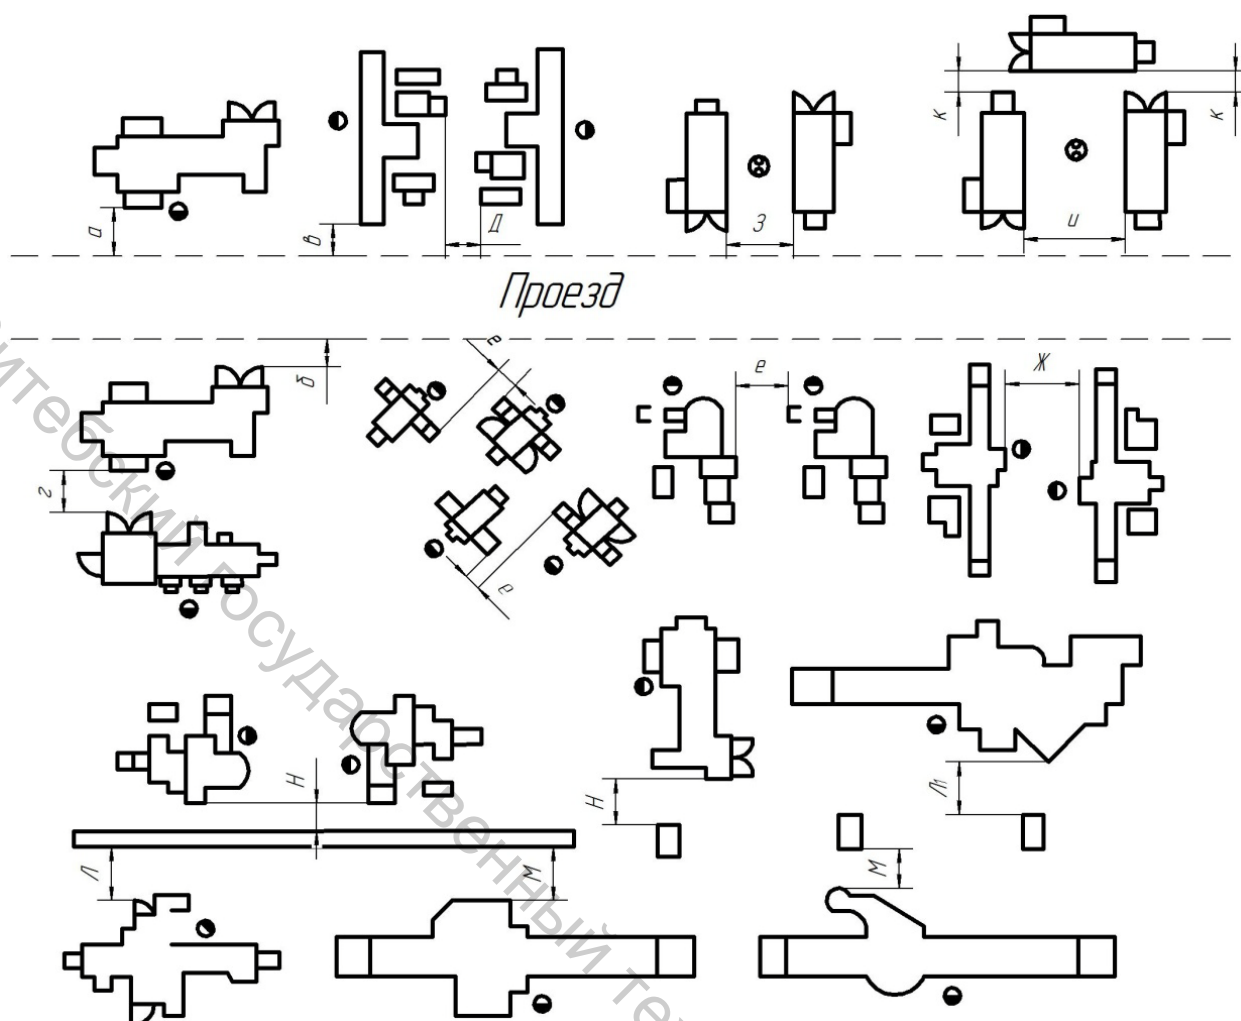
Варианты размещения станков относительно проездов, друг друга, стен и колонн здания
